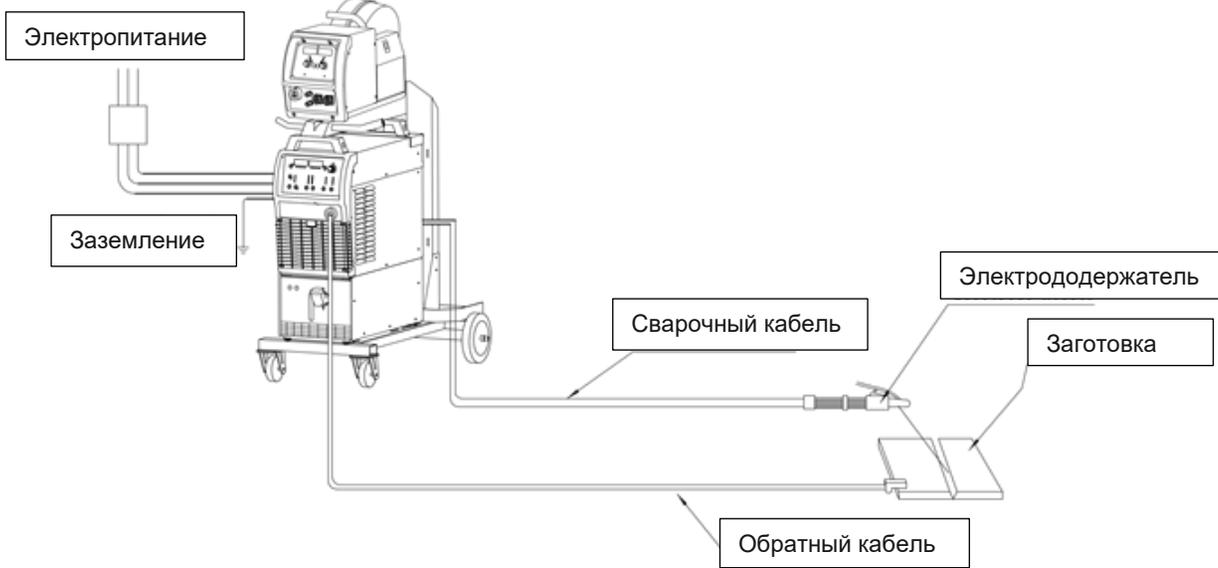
Комплект для ручной дуговой сварки
